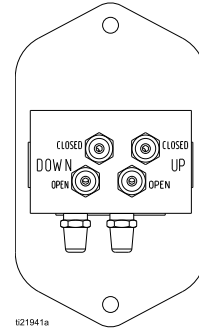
Schlauchanschlüsse am Magnetventilverteiler, zum Pumpeneinlassverteiler
